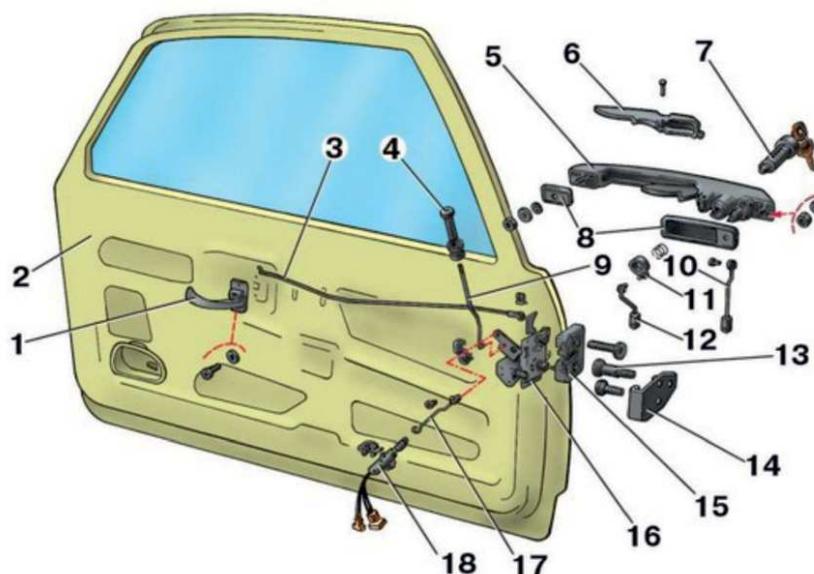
Внутреннее устройство двери автомобиля: 1 – внутренняя ручка двери; 2 – дверь; 3 – тяга внутреннего привода; 4 – кнопка; 5 – наружная ручка двери; 6 – клавиша ручки; 7 – личинка замка; 8 – уплотнитель ручки; 9 – тяга кнопки; 10 – тяга наружного привода; 11 – поводок выключателя замка; 12 – тяга поводка; 13 – «палец» фиксатора замка; 14 – корпус фиксатора замка; 15 – наружный замок; 16 – внутренний замок; 17 – тяга моторедуктора; 18 – моторедуктор блокировки замка двери
